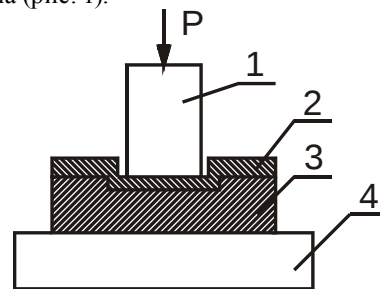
Схема холодной сварки: 1 — пуансон; 2 и 3 — свариваемые детали; 4 — матрица
